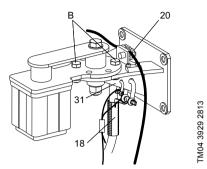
Верхний фиксатор с подъёмным и страховочным тросами и кабельным разъёмом
